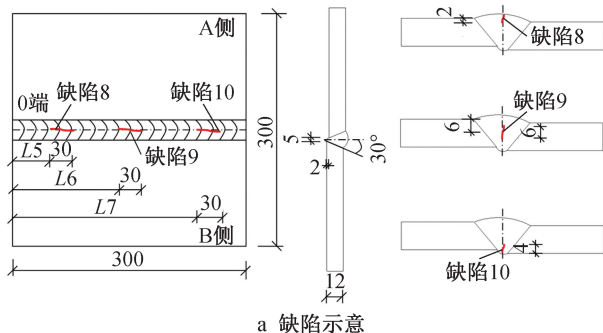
试件 JMHS-221226 焊缝缺陷设置
